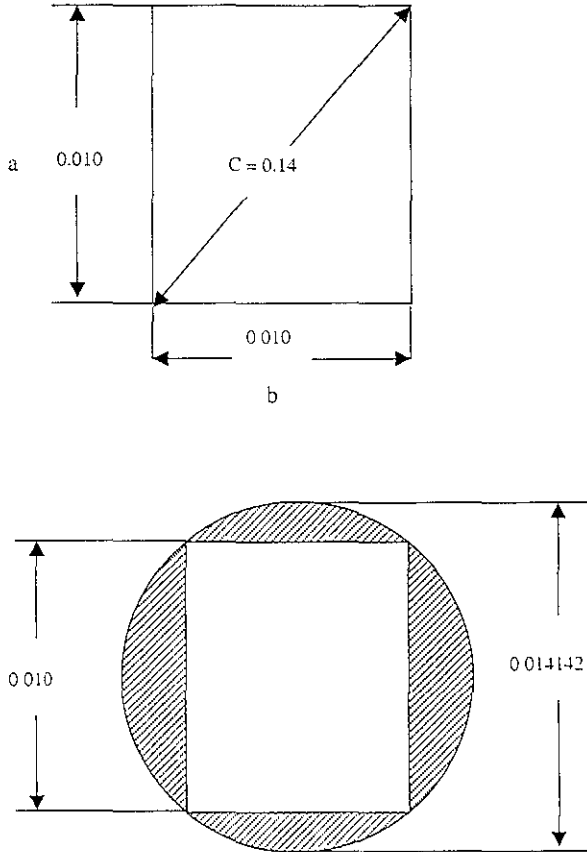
Determinación de la zona cilíndrica de tolerancia geométrica usando el teorema de Pitágoras (dim. en pulg.).
